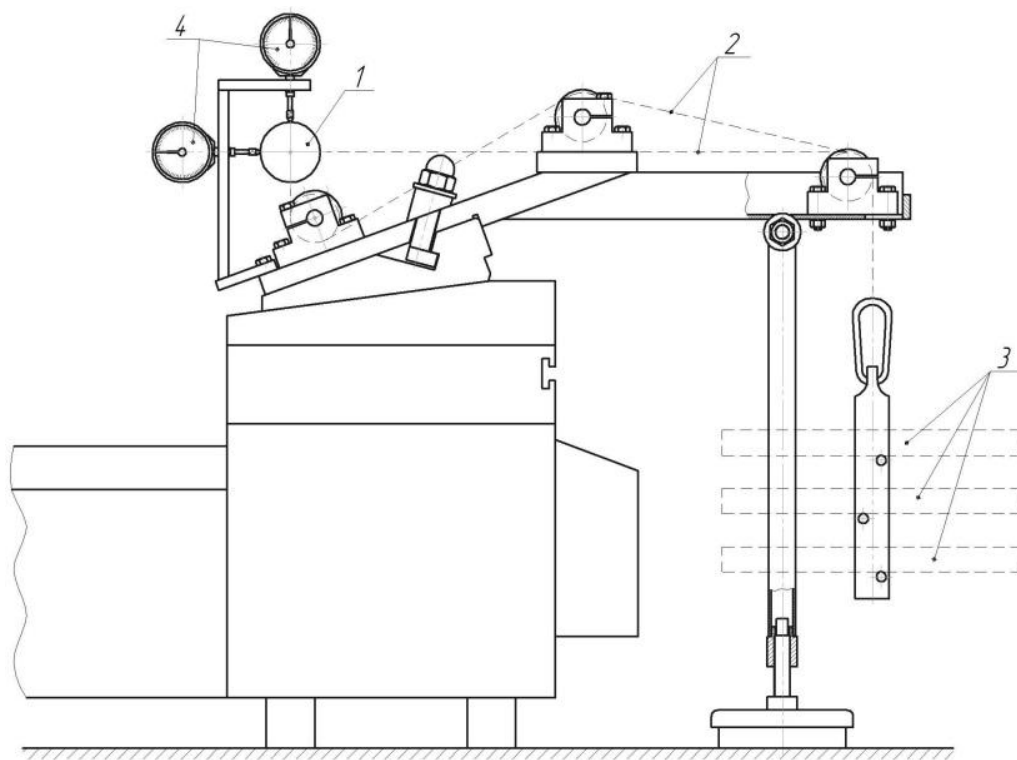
Приспособление для тарировки силоизмерительного устройства
